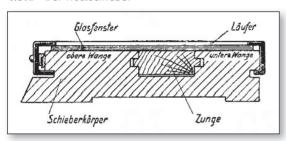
Die Holl'schen Bezeichnungen am Querschnitt des Holzschiebers (Quelle: Holl 1908-1, Tafel I, Fig. 3)
